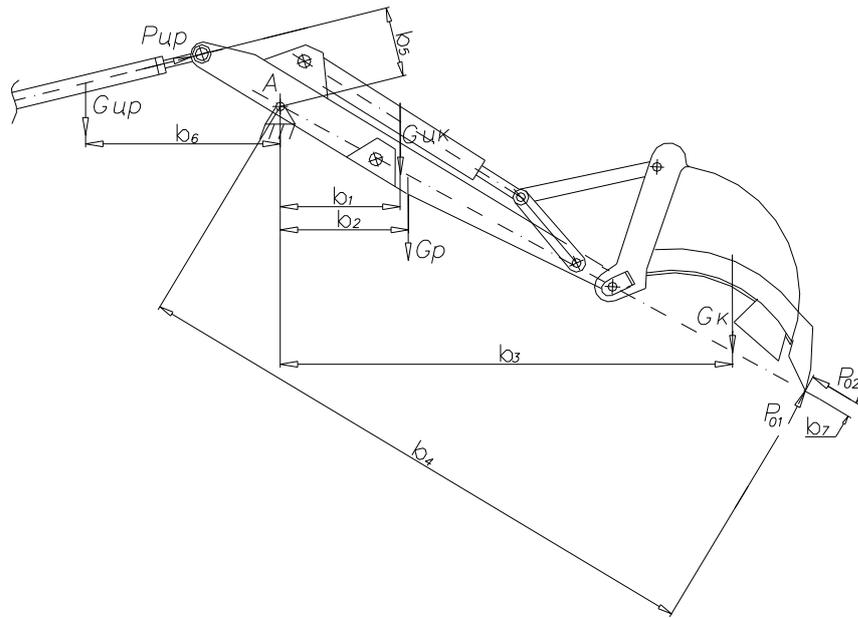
Расчётная схема для расчёта усилия в гидроцилиндре рукояти
